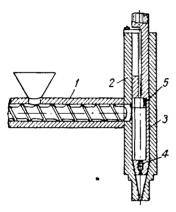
Схема одного из вариантов трехступенчатой литьевой машины:
